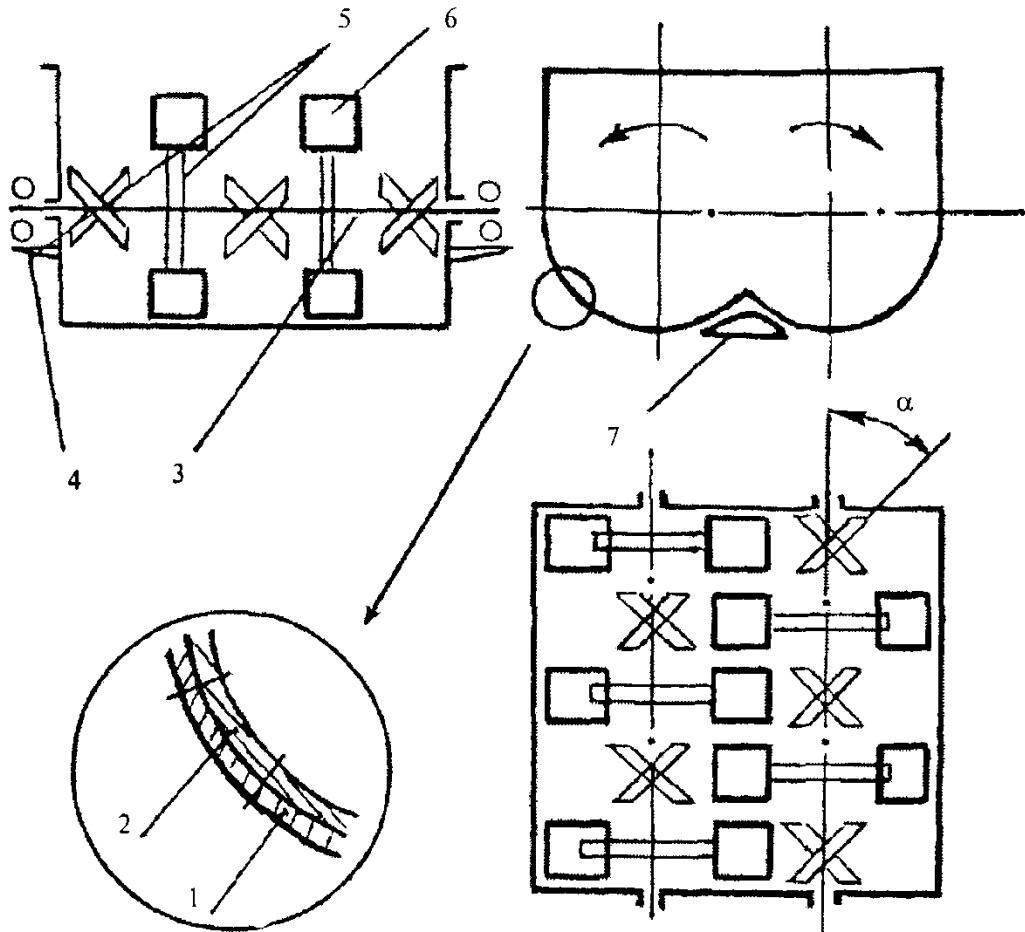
Схема двовального лопатевого змішувача: 1 – корпус; 2 – футерування; 3 – вал; 4 – опора вала; 5 – кронштейн; 6 – лопать; 7 – затвор;  $\alpha$  – кут установлення лопатей
